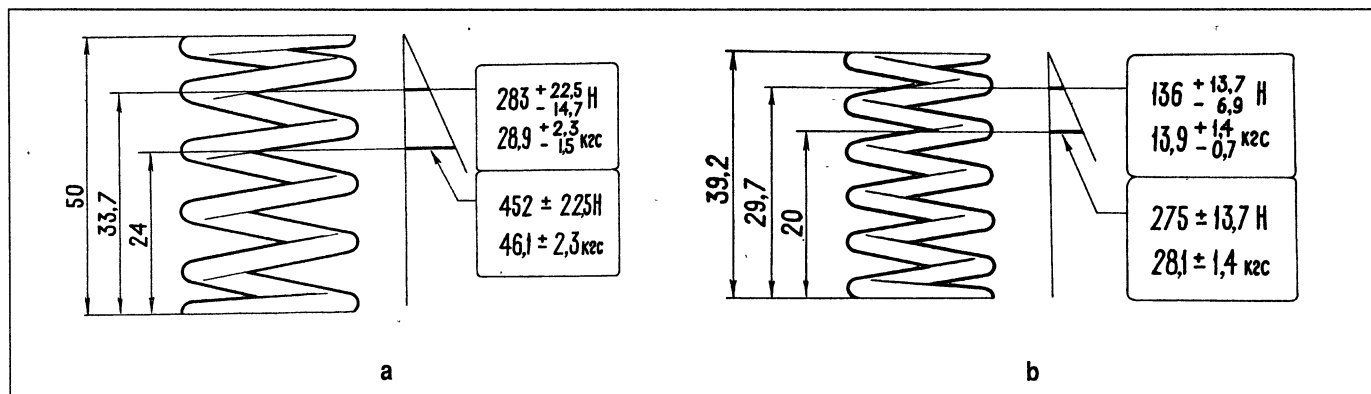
Основные данные для проверки наружной (а) и внутренней (б) пружины клапана
